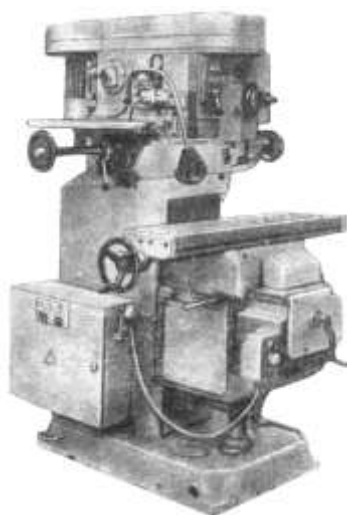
Вертикальный консольный шпоночно-фрезерный станок 692Р
